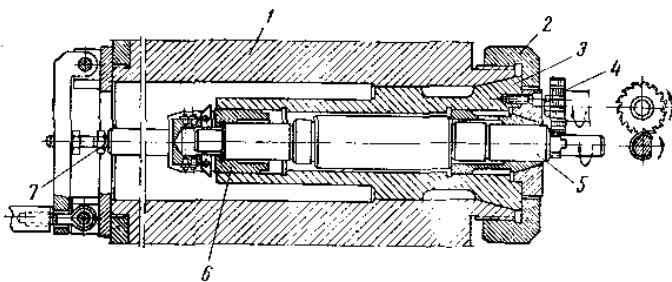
Наладка резьбофрезерного станка с заготовкой, установленной через шпиндель станка:
